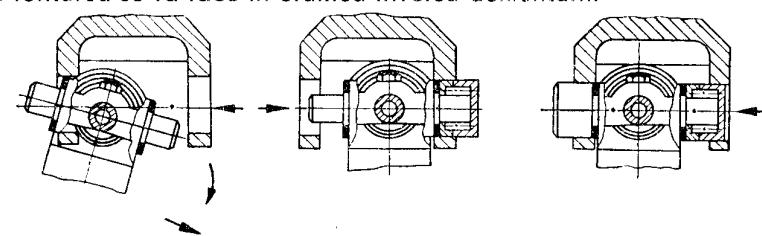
Ordinea de montaj a rulmenților cardanului.
